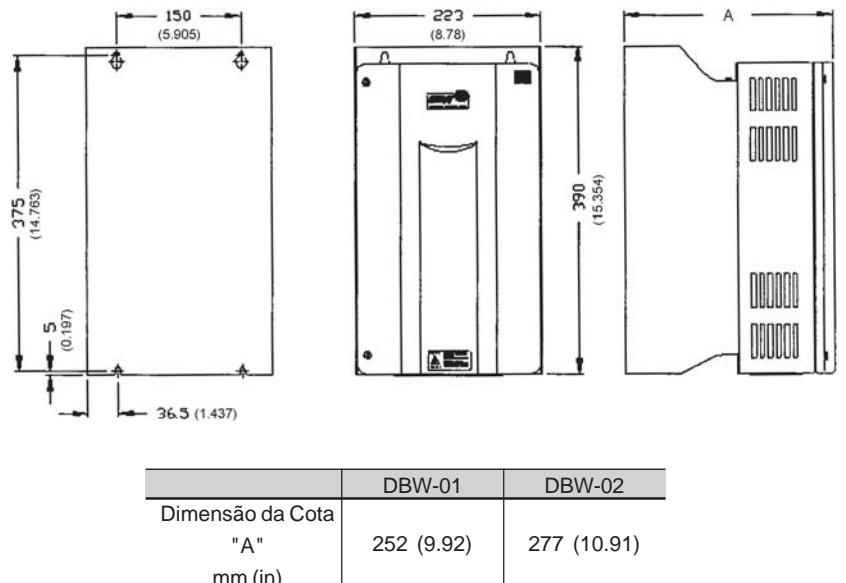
Dimensional para DBW-01 e DBW-02
